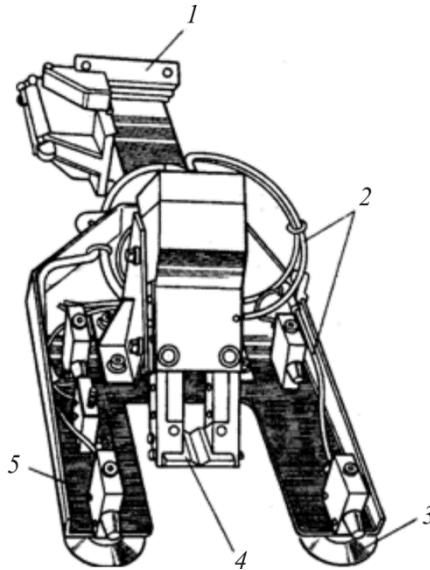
Вакуумное захватное устройство для съема изделий с термопластоавтоматов с пневматическими ножницами для отрезки литников [14]: 1 – хвостовик ЗУ; 2 – пневмопровода; 3 – вакуумная присоска; 4 – пневматические ножницы; 5 – рама
